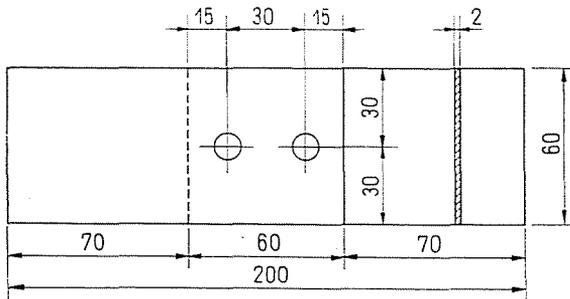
Zweipunkt-Schweißverbindung
